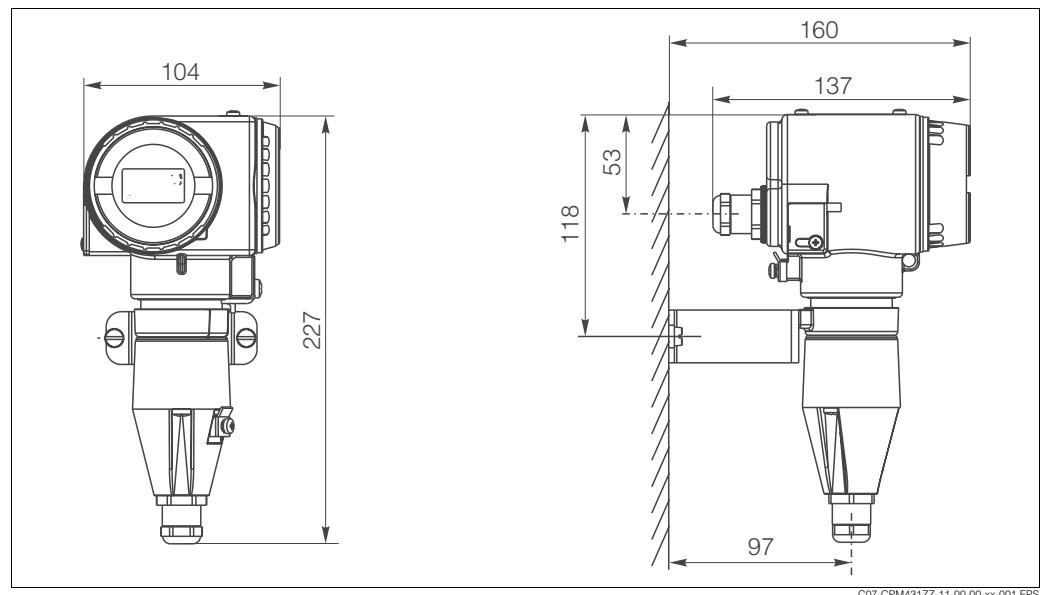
MyPro für Wandmontage mit Befestigungsbügel (bei CXM431-xxx2xx im Lieferumfang)
